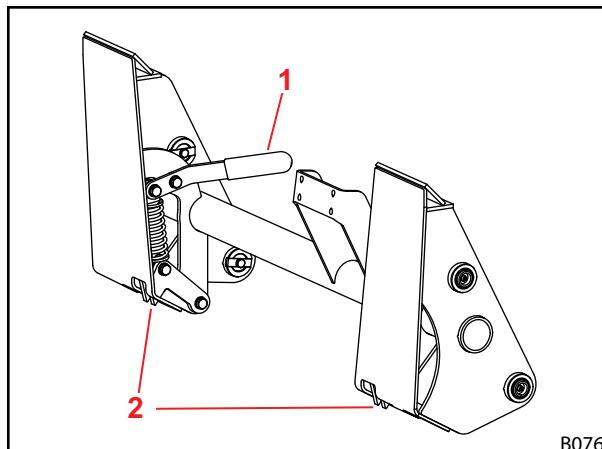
Werkzeug-Verriegelung am Skid-Steer-Wechselrahmen
